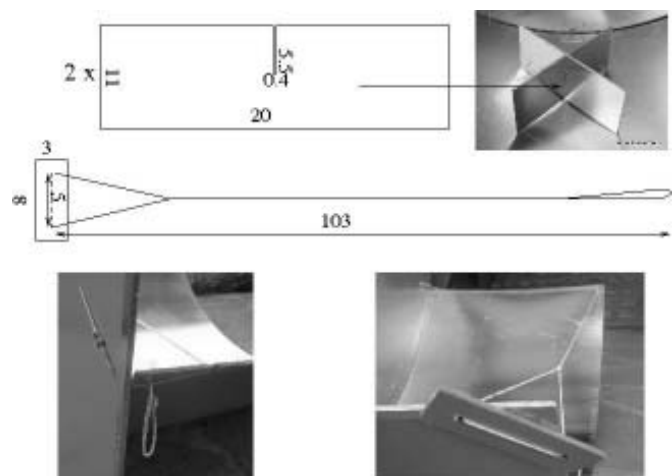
Detalles de las planchas para el soporte y el dispositivo de encastre.
